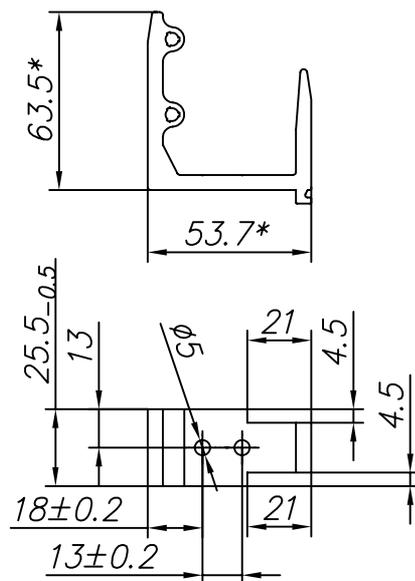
Изготовление соединителя FLGU.400.0913
